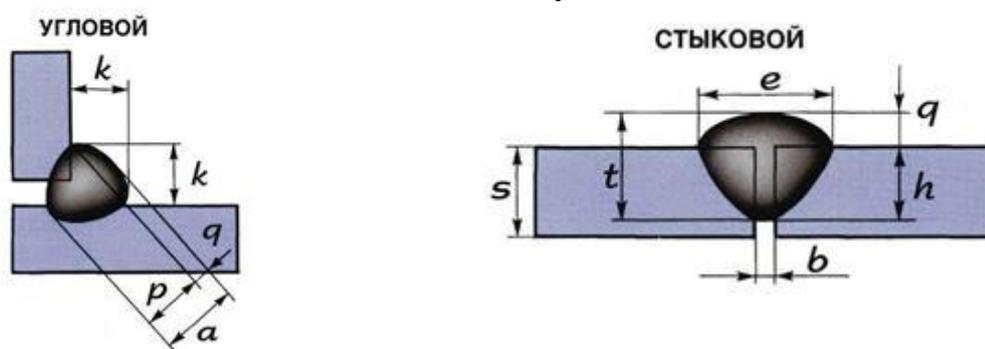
Конструктивные размеры сварного шва
